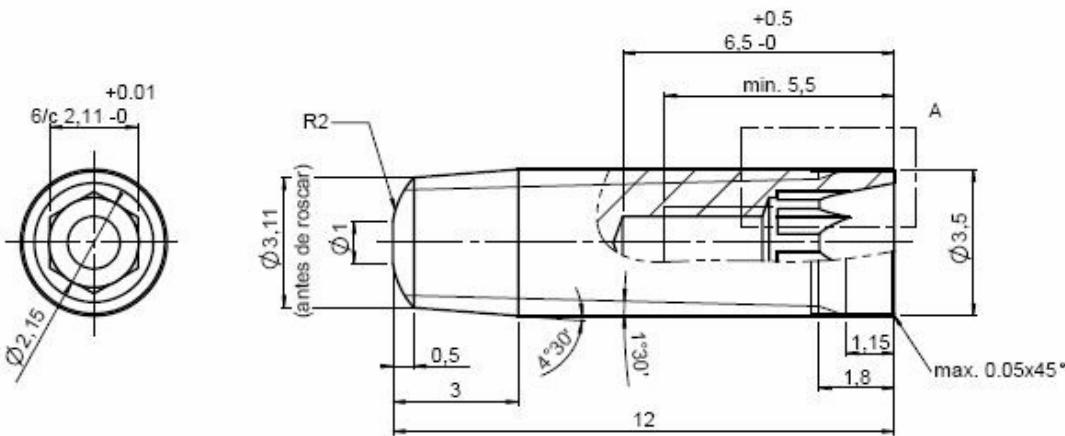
Descripción geométrica del implante SURGIMPLANT IPX gr IV
